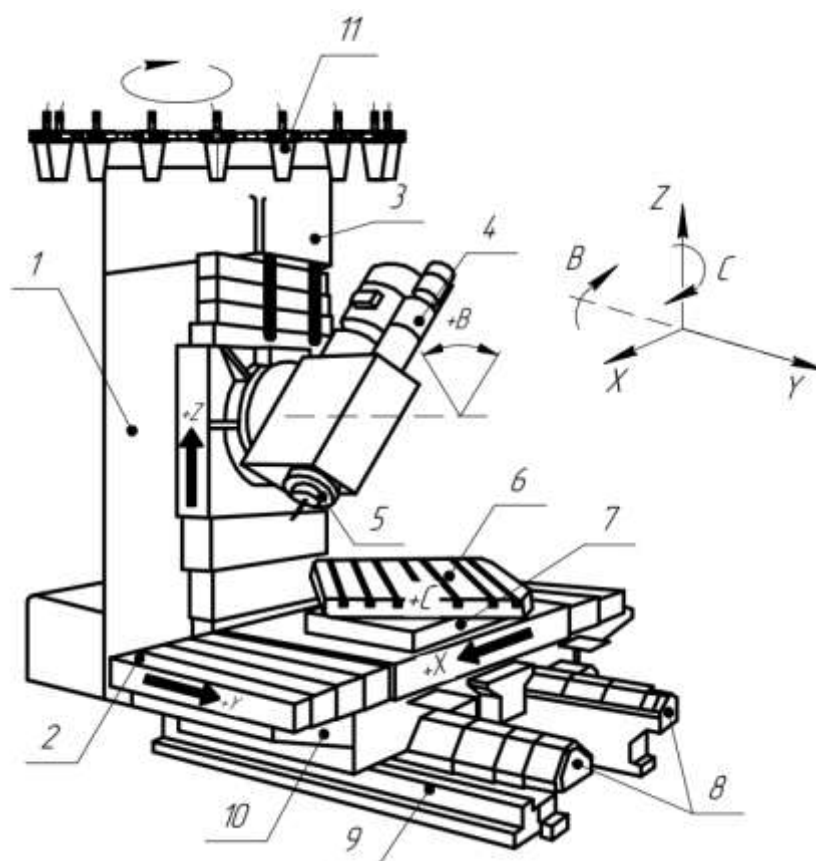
Эскиз малогабаритного пятиосевого фрезерного станка:
